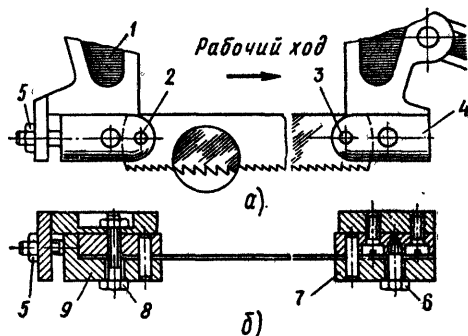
Установка ножовочного полотна: а — установка полотна, б — натяжение полотна; 1 — пильная рама, 2 — штифт подвижной планки, 3 — штифт неподвижной планки, 4 — неподвижная планка, 5 — гайка, 6, 8 — болты, 7, 9 — накладные планки
